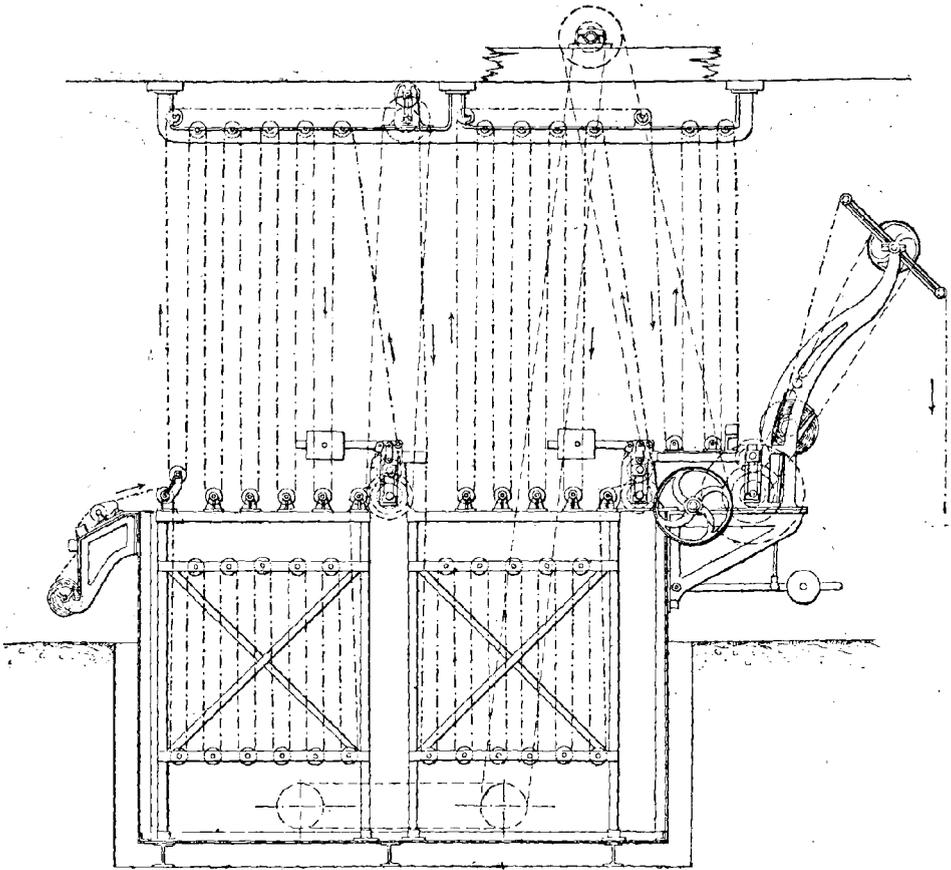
Cuve continue à teindre en indigo; construction Welter.
